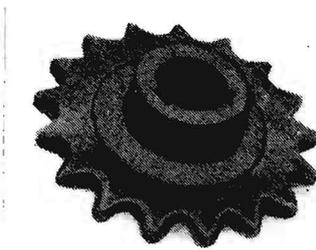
Feingschmiedetes Kettenrad (bis auf Bohrung)
